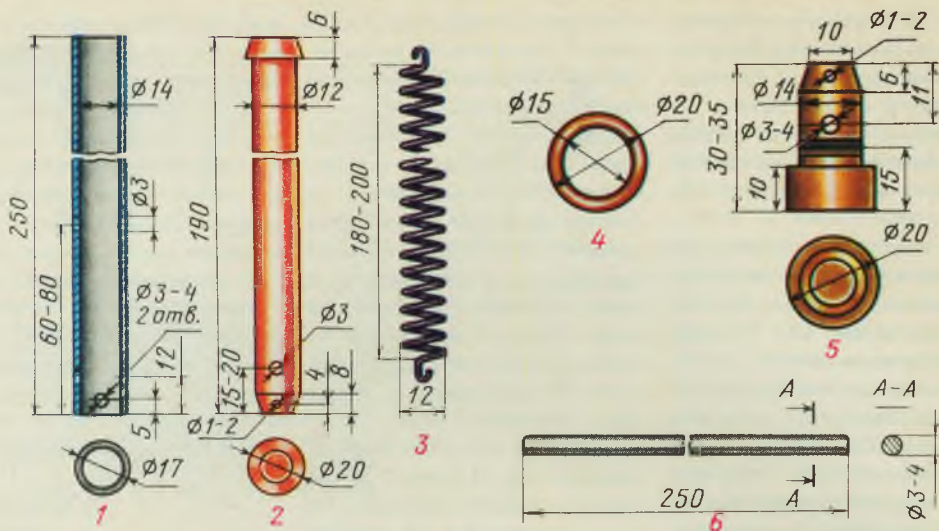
Детали удочки: 1 — корпус; 2 — шток-сигнализатор; 3 — пружина; 4 — зажимное кольцо; 5 — пробка; 6 — упор.
